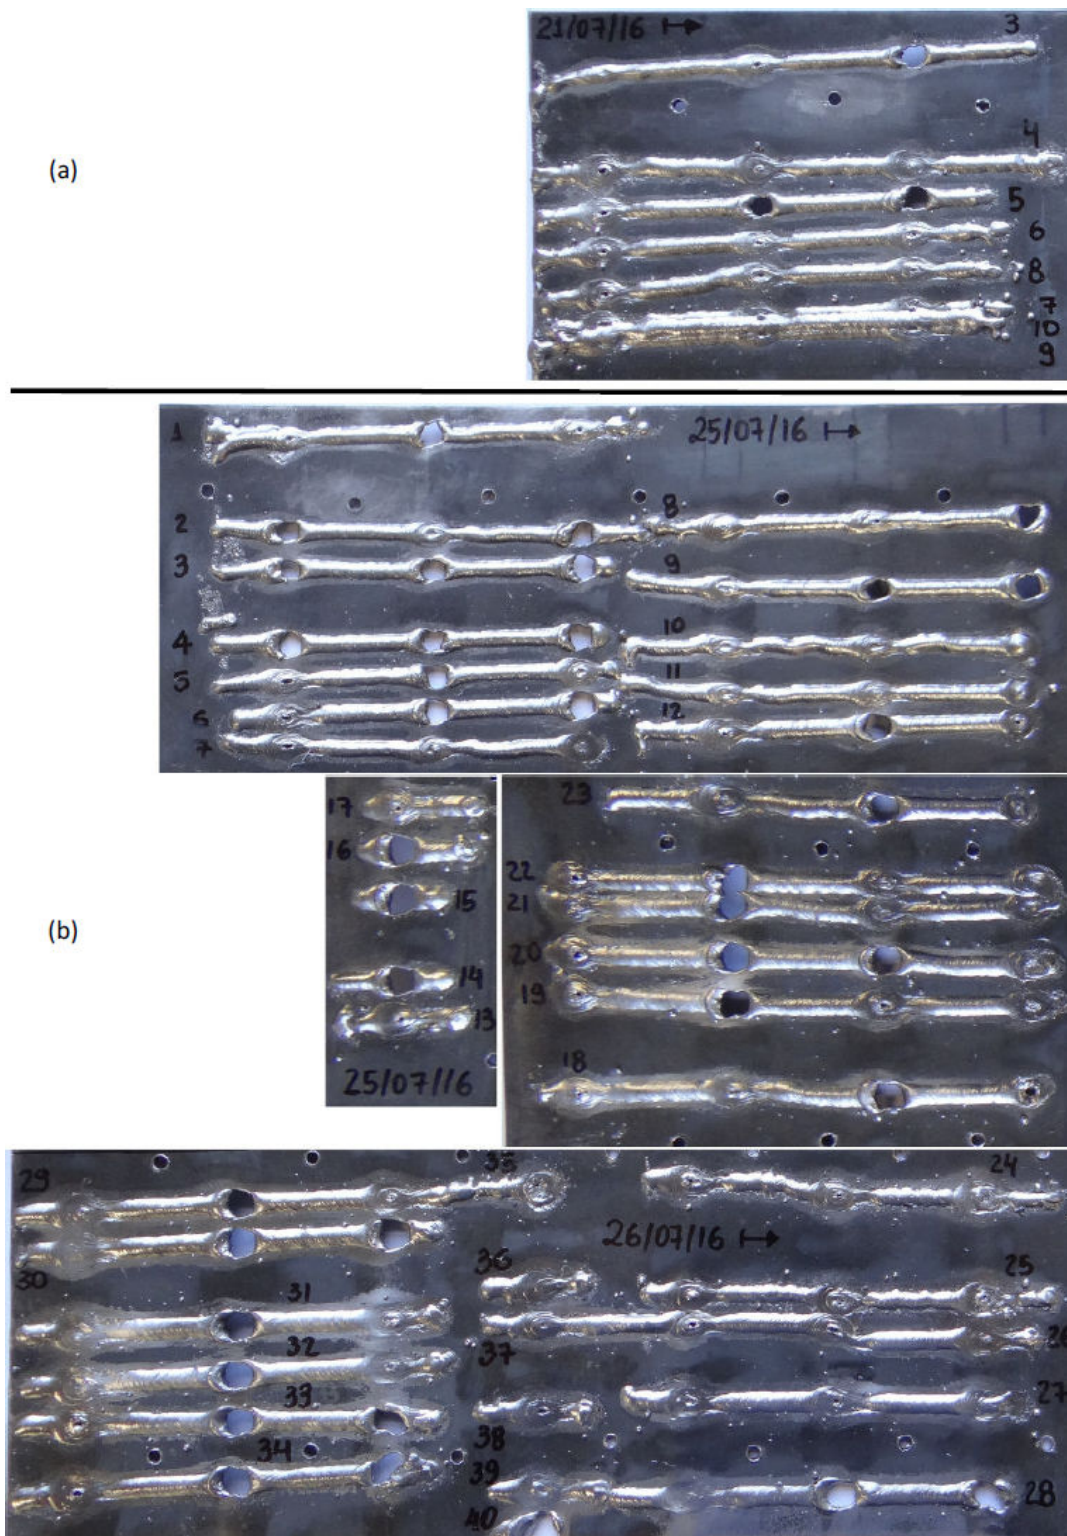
Cordões de solda executados por meio da estação de soldagem SMAW robotizada: (a) efetuados para otimizar os parâmetros de soldagem; (b) utilizados nos classificadores. Fonte: Autor.
